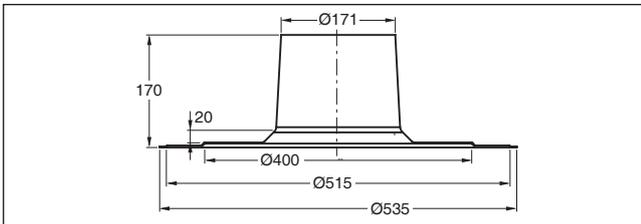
Flachdach-Klebeflansch für DN 110/160 (Maße in mm)
